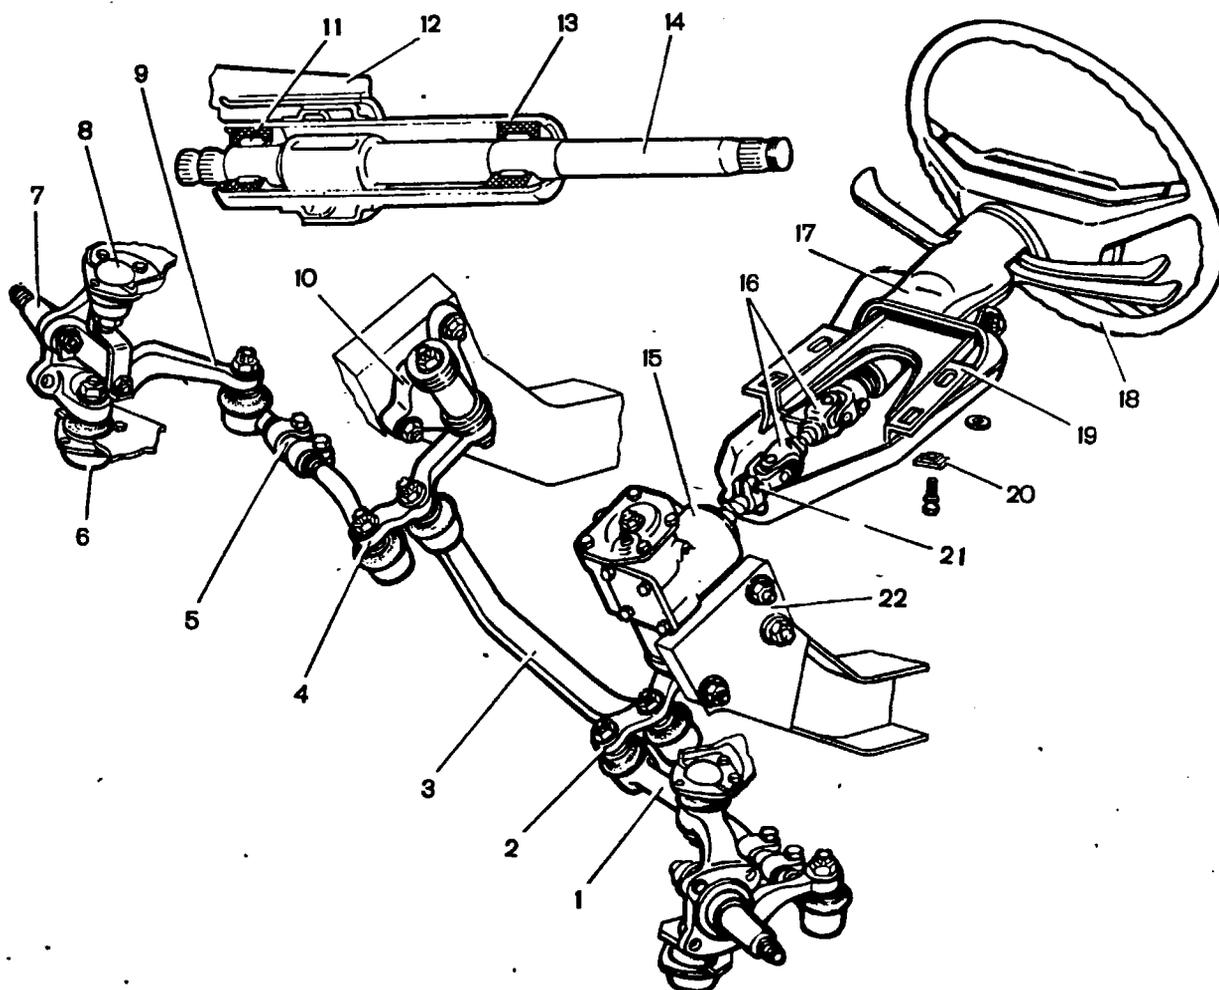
Рулевое управление: 1 - боковая тяга; 2 - сошка; 3 - средняя тяга; 4 - маятниковый рычаг; 5 - регулировочная муфта; 6 - нижний шаровой шарнир передней подвески; 7 - правый поворотный кулак; 8 - верхний шаровой шарнир передней подвески; 9 - правый рычаг поворотного рычага; 10 - кронштейн маятникового рычага; 11 - подшипник верхнего вала рулевого управления; 12, 19 - кронштейн крепления вала рулевого управления; 13 - труба кронштейна крепления вала рулевого управления; 14 - верхний вал рулевого управления; 15 - картер рулевого механизма; 16 - промежуточный вал рулевого управления; 17 - облицовочный кожух вала рулевого управления; 18 - рулевое колесо; 20 - фиксирующая пластина передка кронштейна; 21 - стяжной болт крепления карданного шарнира; 22 - лонжерон кузова
